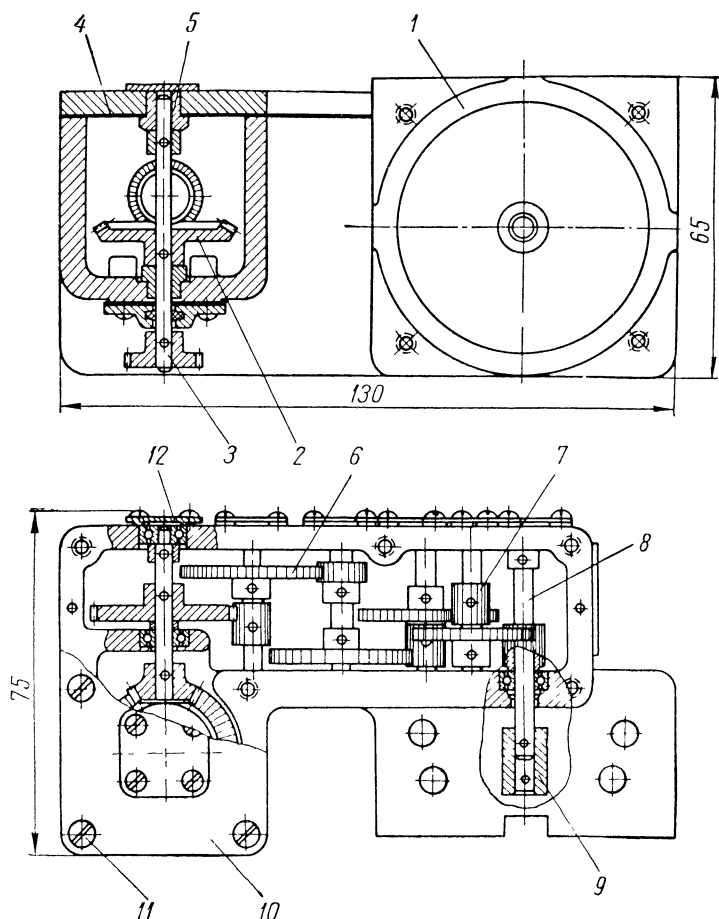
Конструкция редуктора в закрытом литом корпусе
